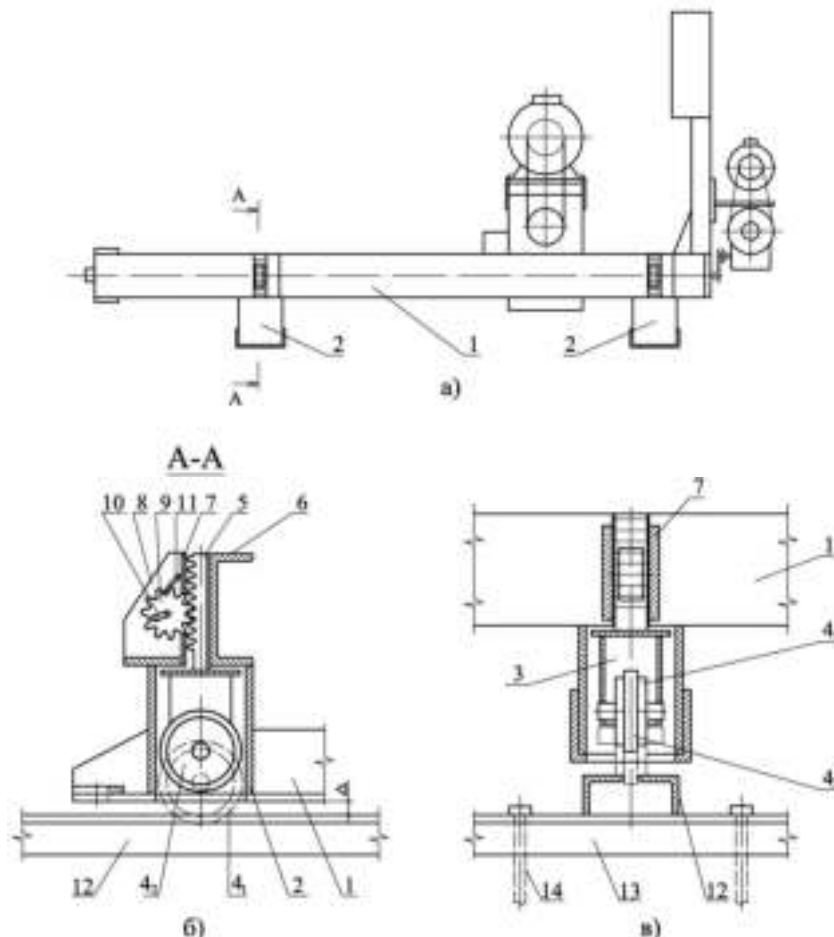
Механізм переміщення бурового станка по рейковим напрямним: а) загальний вид станка; б) розріз А-А; в) вид збоку; 1 – станина; 2 – циліндр; 3 – корпус; 4 – ролик кочення; 4₁ – крайні опорні вінці; 4₂ – середня частина ролика; 5 – зубчата рейка; 6 – боковина станини; 7 – ребро; 8 – косинка; 9 – зубчате колесо; 10 – рукоятка; 11 – фіксатор; 12 – кутникові напрямні; 13 – шпали; 14 – штирі
